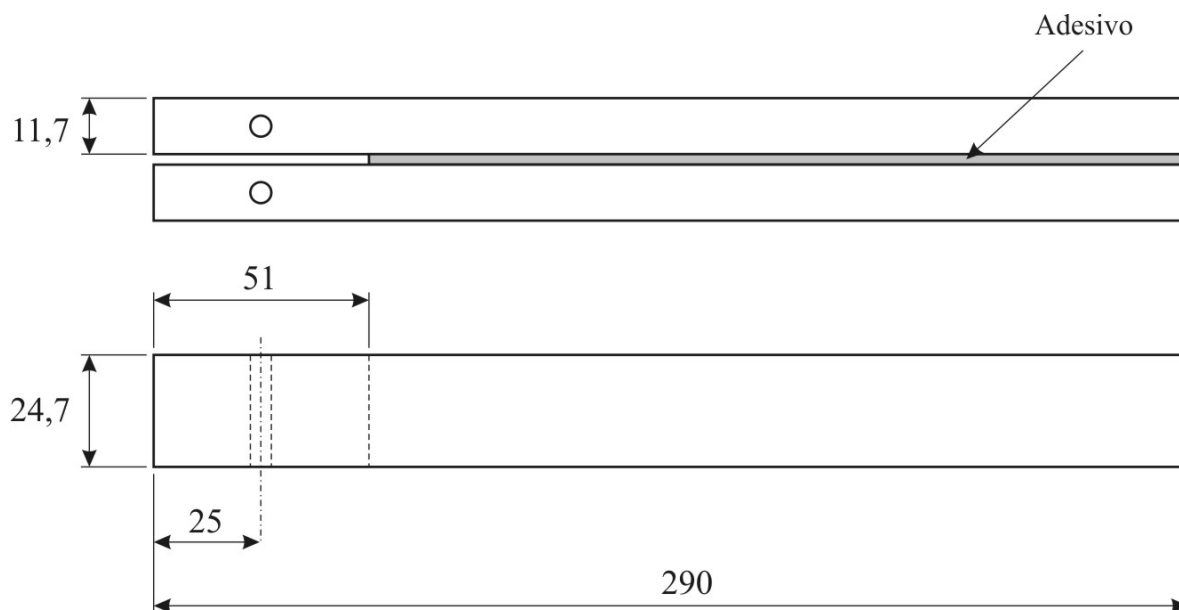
Geometria e dimensões (em mm) do provete DCB (ASTM D3433-99).
